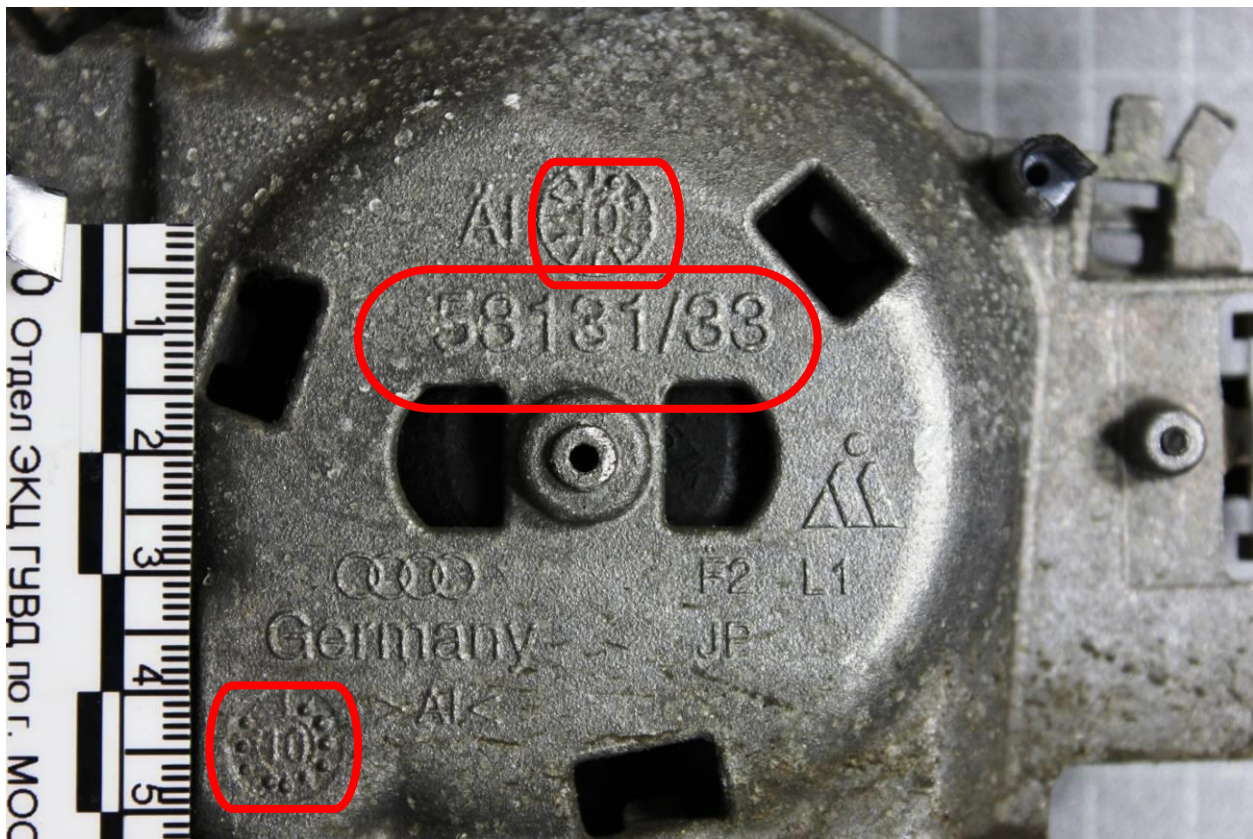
Внутренняя сторона корпуса двигателя электрического привода зеркала заднего вида неустановленного транспортного средства (контурными линиями выделены обозначения года изготовления части ТС и каталожный номер)
